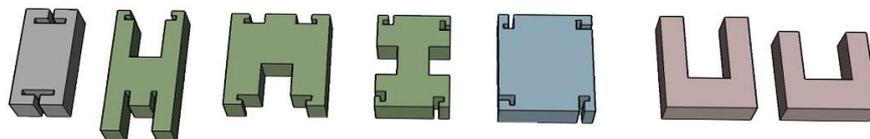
Desenho das peças de viga (cinza), conexões (verde), pilares (azul) e de base (rosa). Fonte: Autores.
